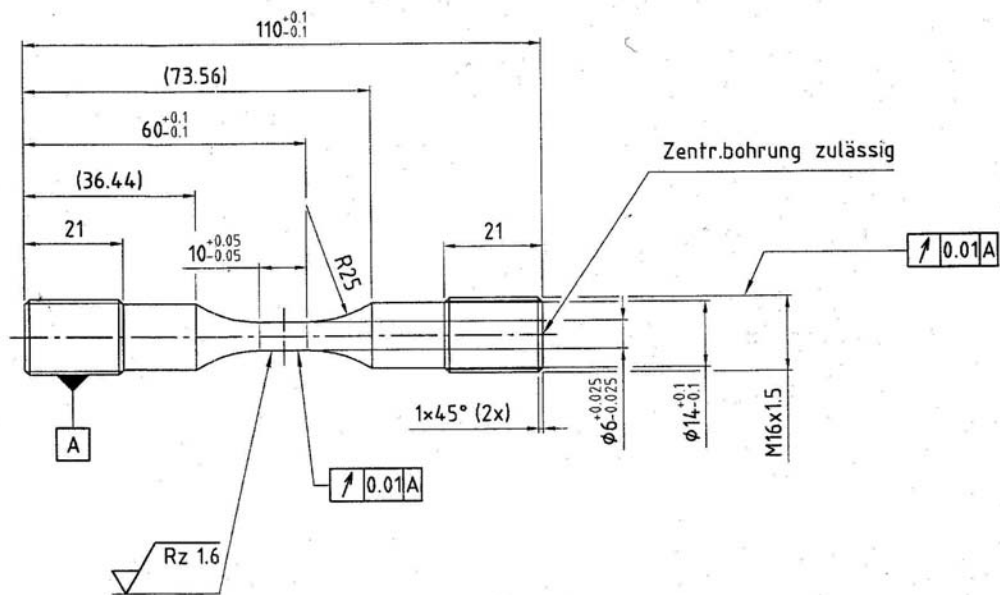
EN AW-6082-T5, $K_f=1$, Probe für die servohydraulische Prüfmaschine
